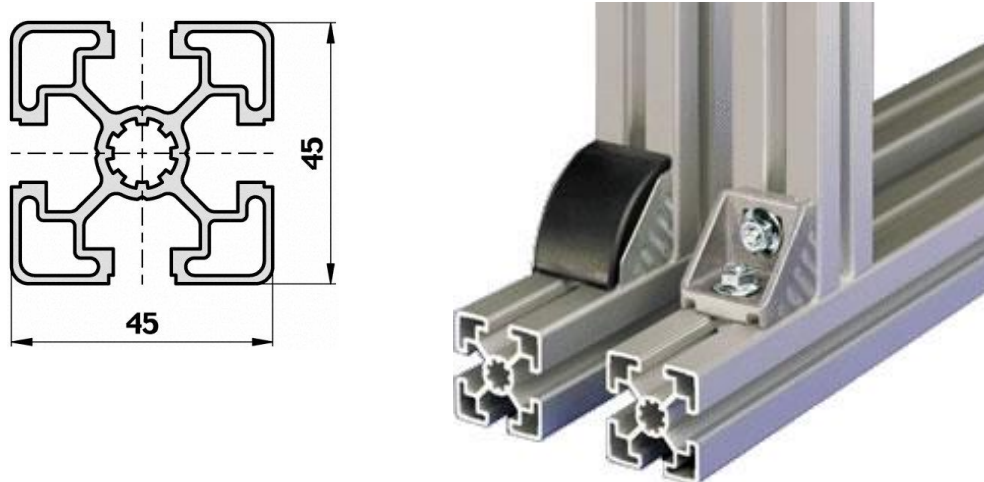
Perfil de aluminio extruido y sección transversal con dimensiones.
